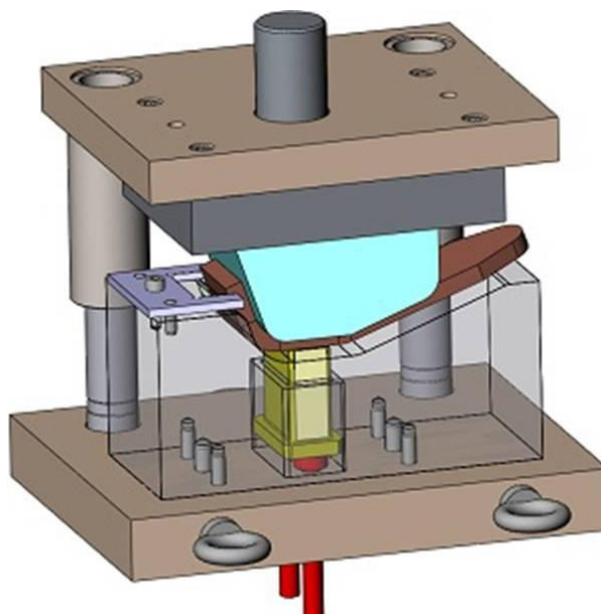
Гибочный штамп для получения изделия волнистого профиля из плоской заготовки
